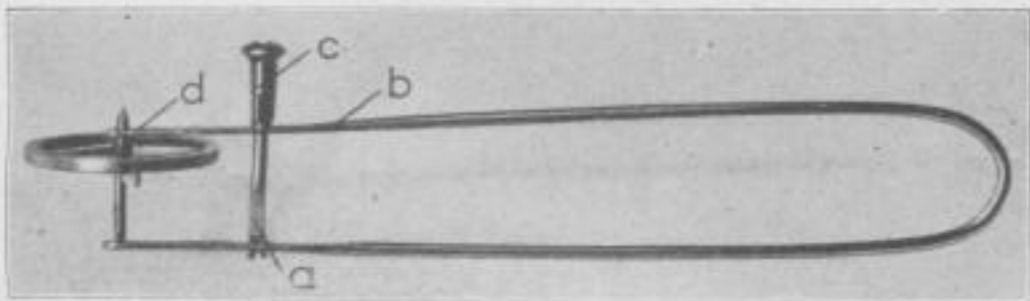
Werkzeug zum Schleifen von Körnerspitzen
